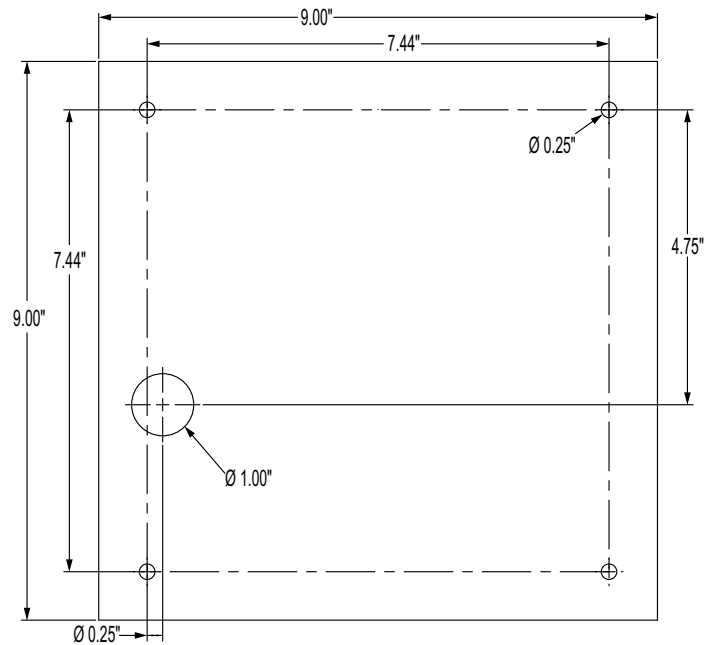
Dimensiones para el montaje en panel del visor de 7" (con teclado)
